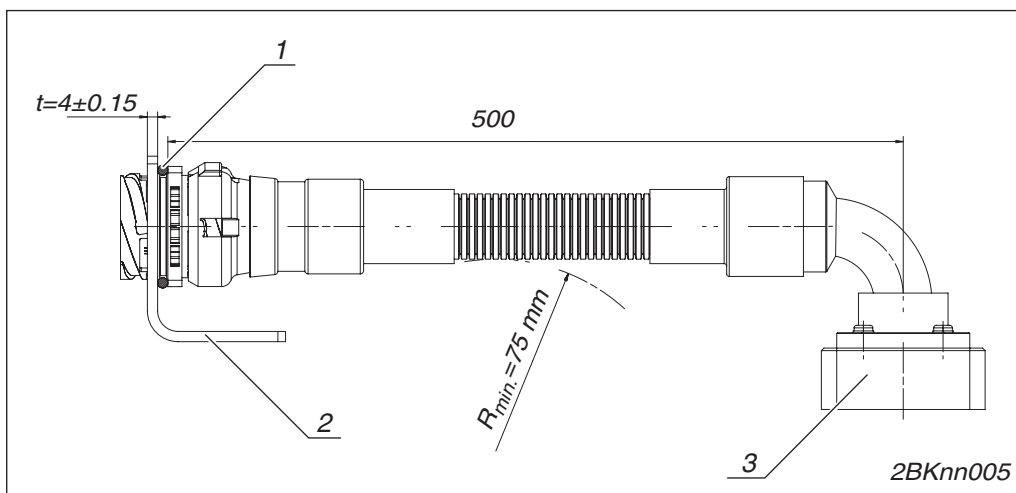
Steckverbindung Getriebe Kabeldurchführung - Getriebekabel (Kabel1)
